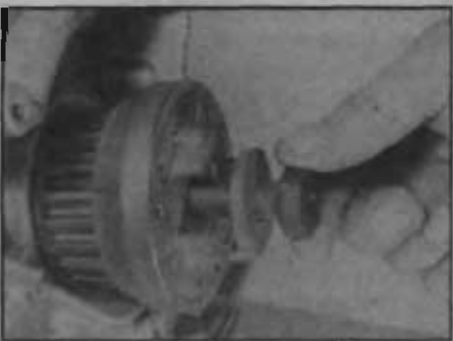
Снятие болта и шайбы крепления шкива зубчатого ремня к коленчатому валу
